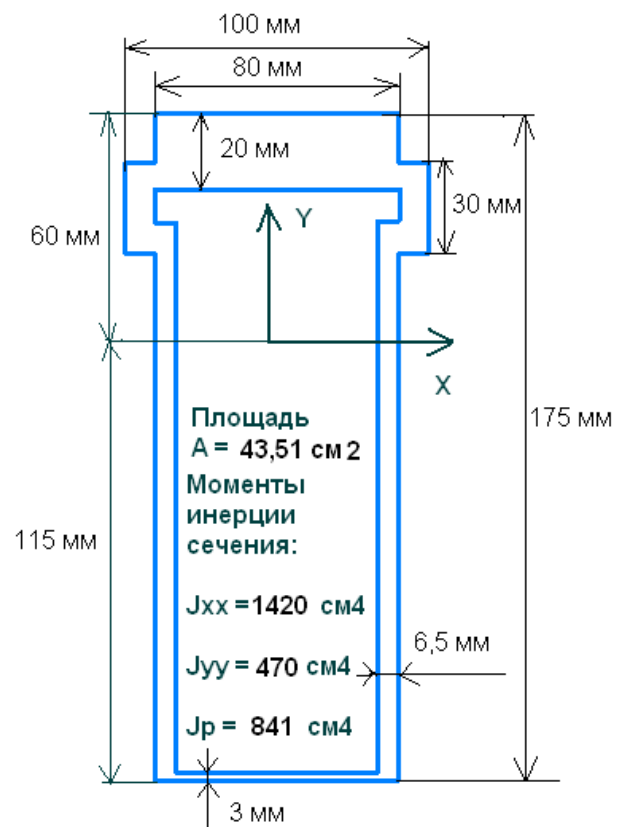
Расчетное поперечное сечение корпуса рельса
